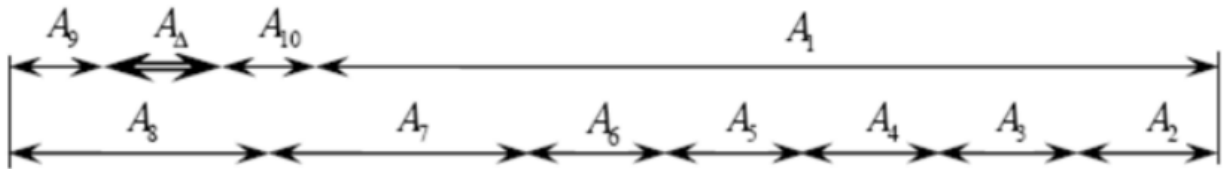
Lanțul dimensional al reductorului precesional de tipul A^B ex-cv cu un element compensator
